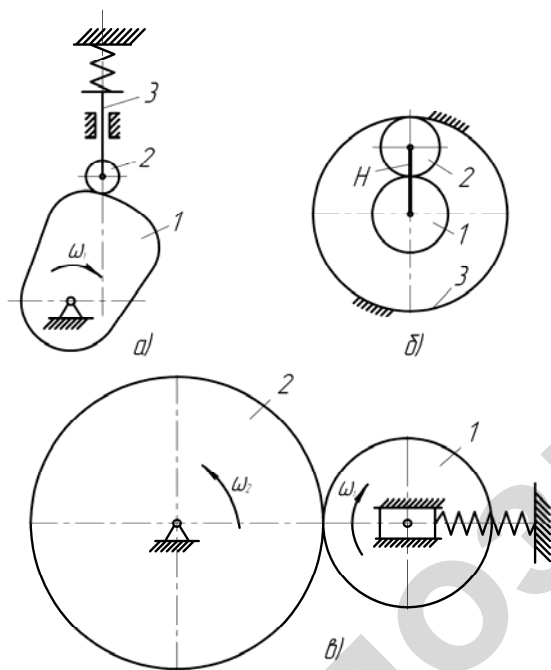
Примеры механизмов: а – кулачковый: 1 – кулачок; 2 – ролик; 3 – толкатель; б – зубчатый планетарный механизм: 1 – солнечная шестерня; 2 – сателлит; 3 – опорная шестерня; H – водило; в – фрикционный механизм: 1 – ведущий ролик; 2 – ведомый ролик
